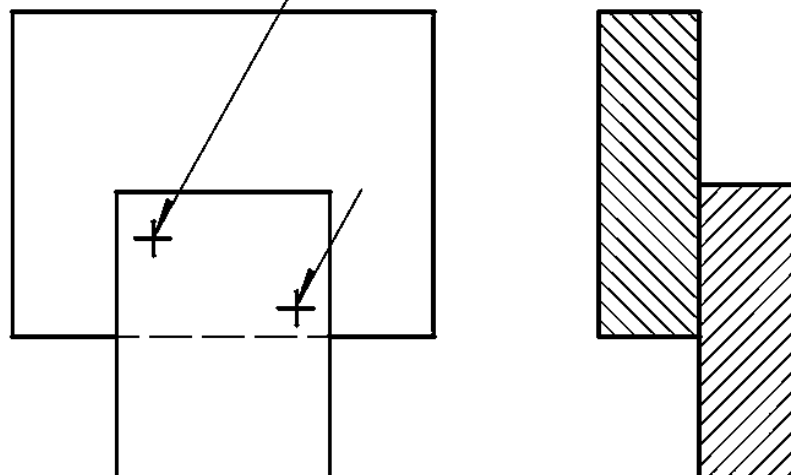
Образец условного обозначения одиночной сварной точки
